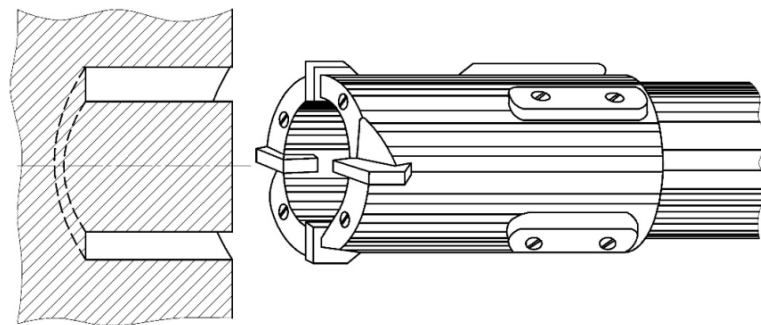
Схема оброблення свердлом для кільцевого свердління
